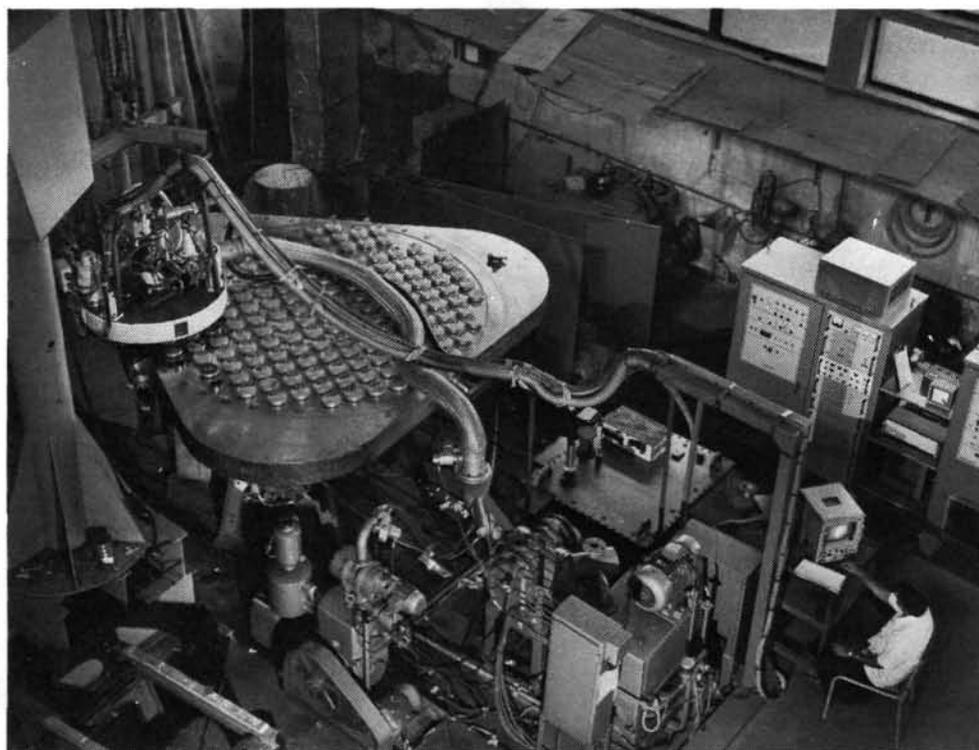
Soudage des tubes de tôle pour la calandre du réacteur de recherche R-5 à l'atelier du BARC.
